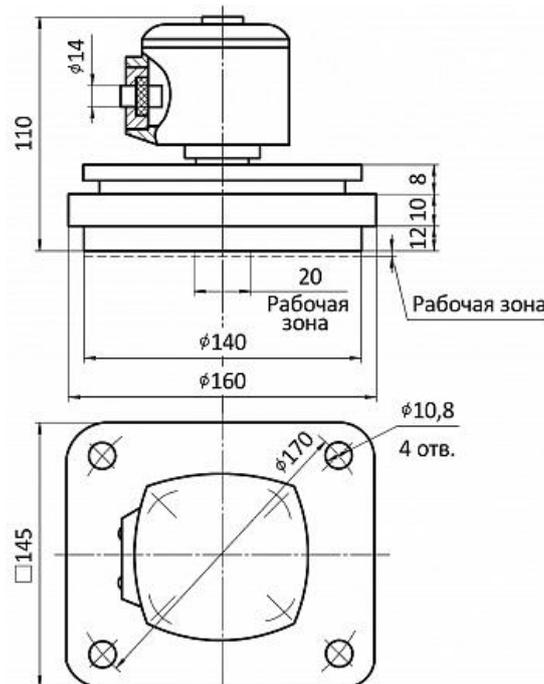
Общий вид, габаритные и установочные размеры СУС-181Р(Б)
